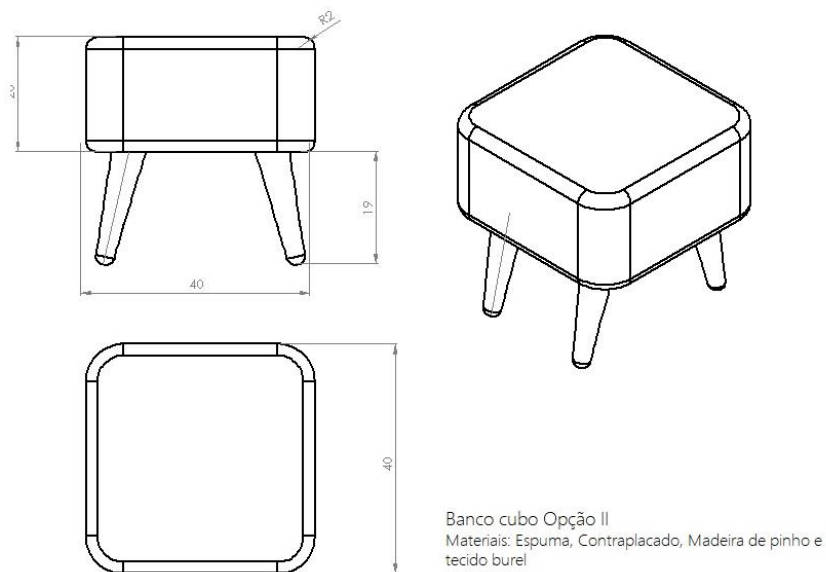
Desenho técnico CAD 3D do banco (Fonte: Autor)
